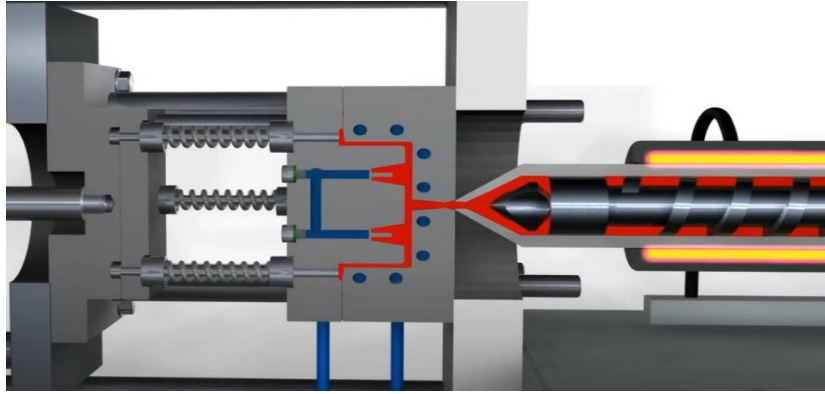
Representação de molde recebendo a massa plástica derretida para moldagem.
